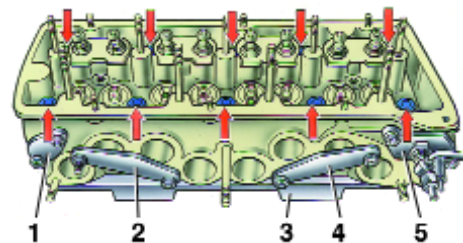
Проверка герметичности головки блока цилиндров на приспособлении: 1, 2 и 4 – заглушки; 3 – плита приспособления; 5 – фланец со штуцером подвода жидкости
